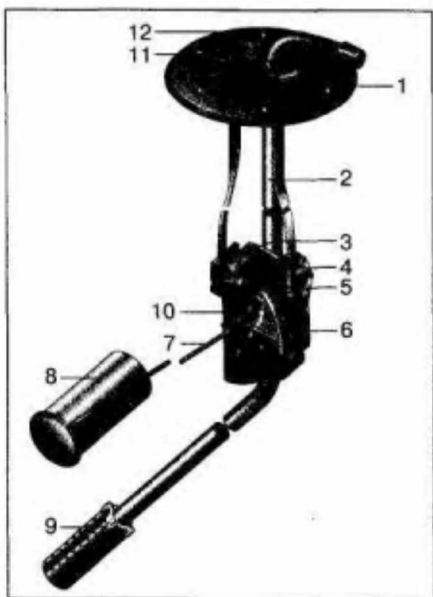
Датчик 34.3827 измерителя уровня топлива: 1 — установочный фланец; 2 — приемная труба; 3 — опорная пластина; 4 — реостат; 5 — контакт включения сигнальной лампы резерва топлива; 6 — ползунок; 7 — рычаг; 8 — поплавок; 9 — сетчатый фильтр; 10 — корпус; 11, 12 — штекеры
